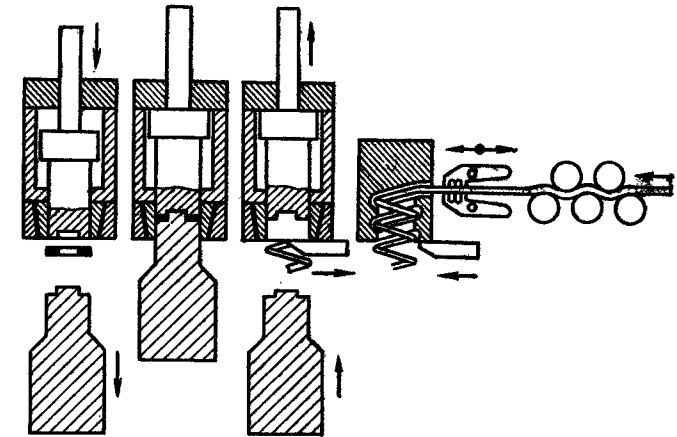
Схема работы автомата для изготовления шайб из проволоки
